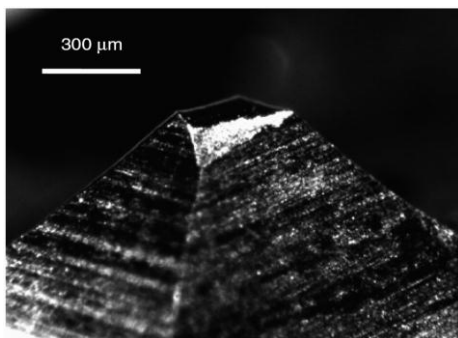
Износ режущей кромки зуба рашпильной фрезы
